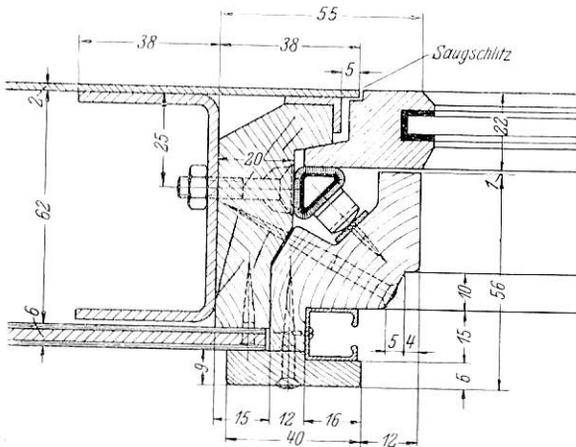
Windschnittiges Fenster mit Saugschlitz.
